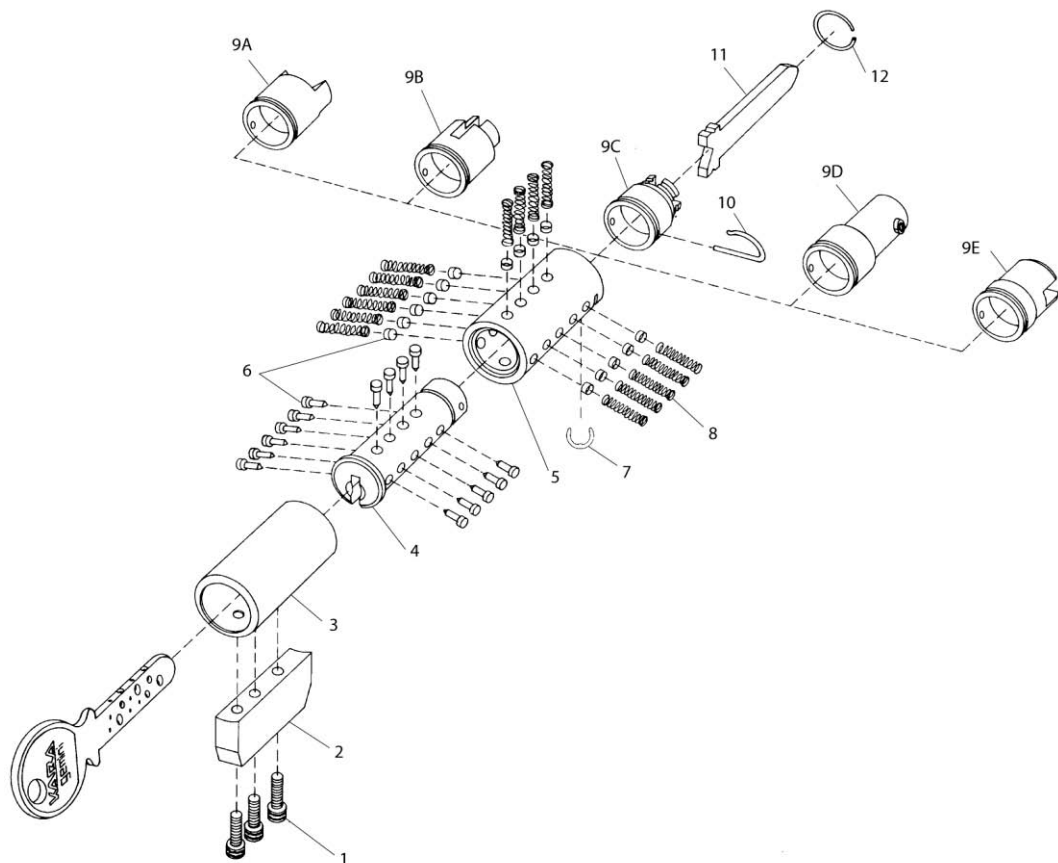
Базовая конструкция цилиндра Gemini "Build-a-Cylinder": 1 — винты вставки; 2 — вставка; 3 — втулка; 4 — личина цилиндра; 5 — оболочка цилиндра; 6 — верхние и нижние пины из упрочненной нержавеющей стали; 7 — фиксатор личины; 8 — пружины; 9A — адаптер Sargent integralock; 9B — адаптер Yale; 9C — адаптер Tailpiece; 9D — адаптер Sargent серий "7", "8", "9"; 9E — адаптер Emhart высокой прочности и адаптер блокировки устройства; 10 — фиксатор адаптера; 11 — хвостовик; 12 — фиксатор хвостовика (С разрешения компании Lori Corporation)
